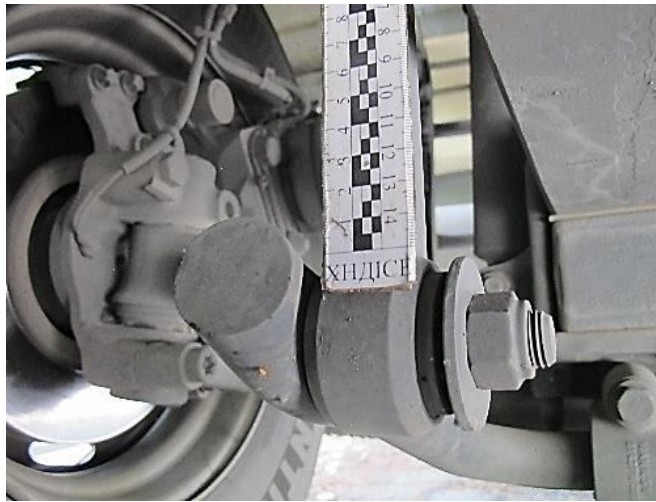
Детальний вигляд кріплення передньої частини повздовжнього важеля підвіски правого переднього колеса автомобіля MAN TGM
